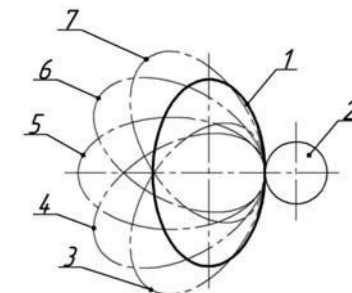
Положения заготовки некруглого зубчатого колеса относительно режущего инструмента: 1 – заготовка, 2 – режущий инструмент, 3, 4, 5, 6, 7 – позиции заготовки
